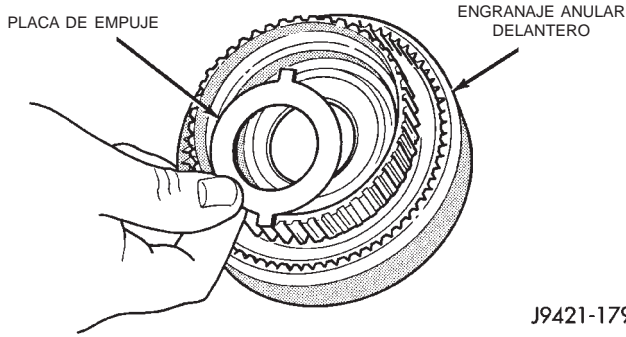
Emplazamiento de la placa de empuje en el soporte del engranaje anular delantero
